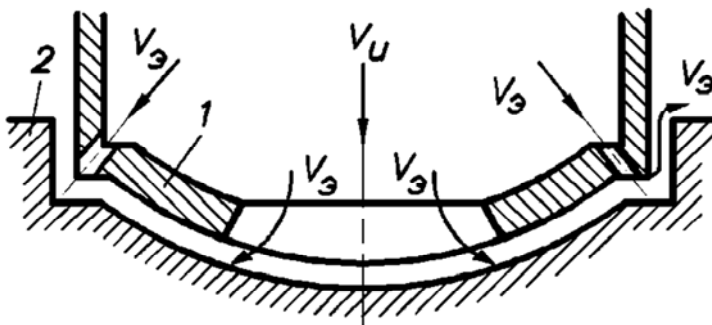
Схема обработки нескольких плавно сопряженных между собой поверхностей сложной формы:
